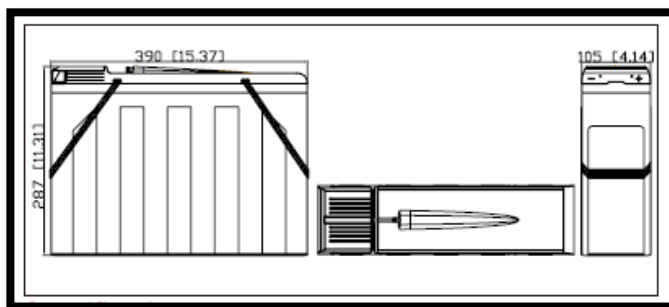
Dimensiones de la batería Narada Fuente: www.merkasol.com
